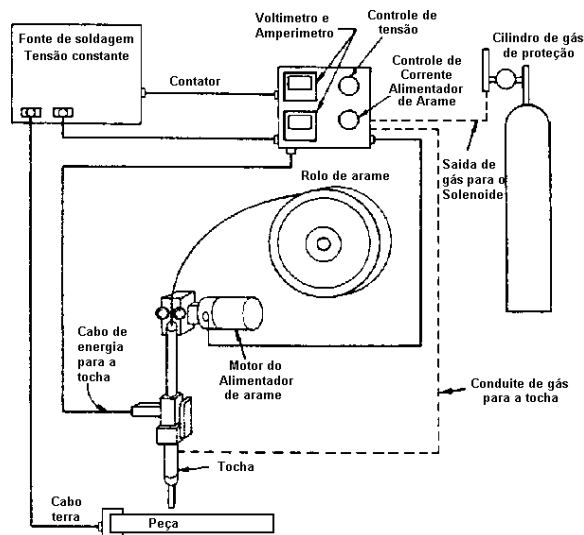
Componentes do equipamento necessário para o processo de soldagem GMAW
